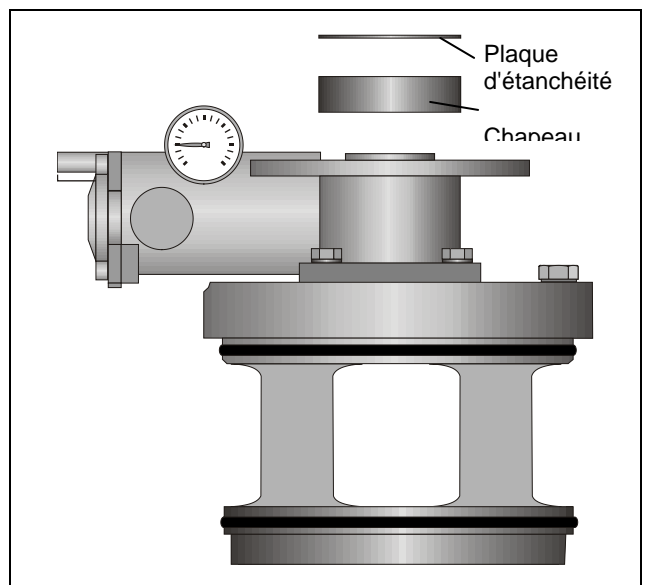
Dépose de la plaque d'étanchéité et du chapeau d'étanchéité
